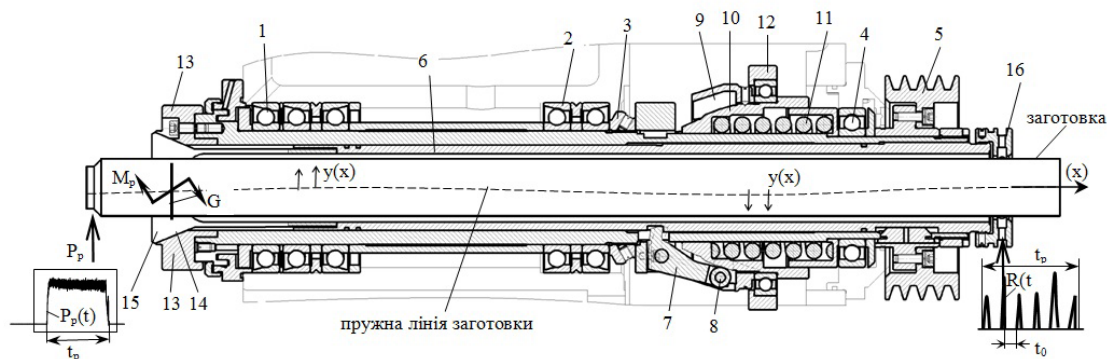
Шпиндельний вузол модуля комплексу ТАК із встановленою в патроні заготовкою
